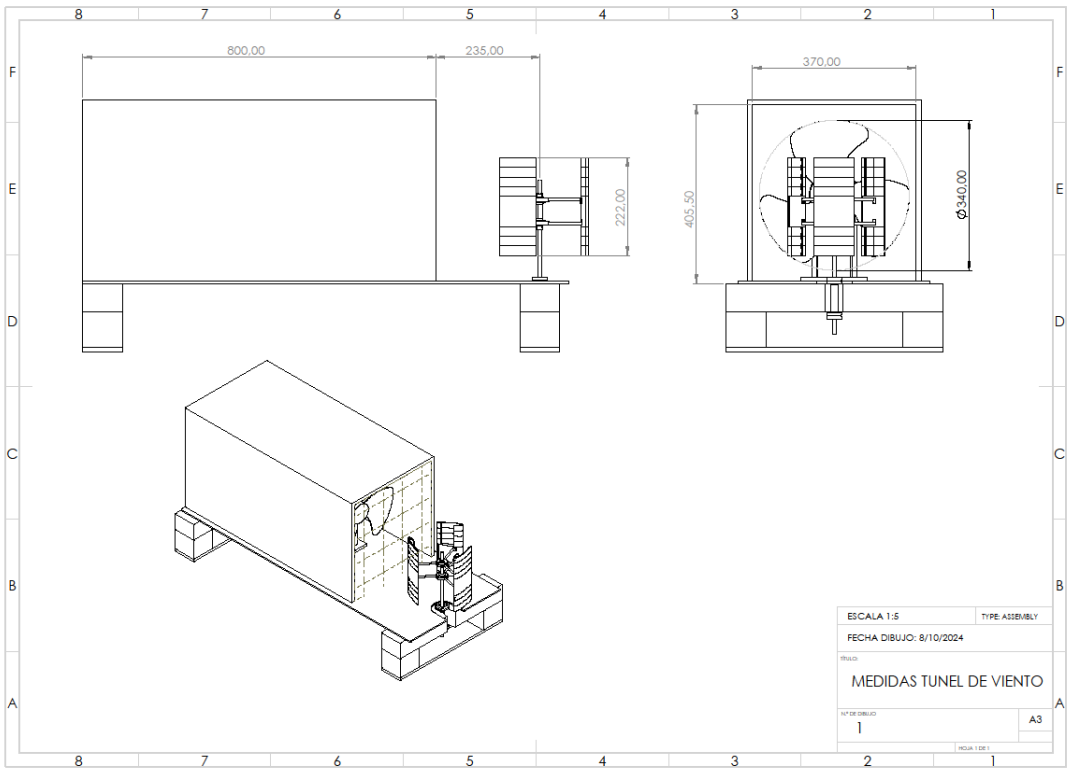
Vistas de montaje: Turbina eólica y túnel de viento.
